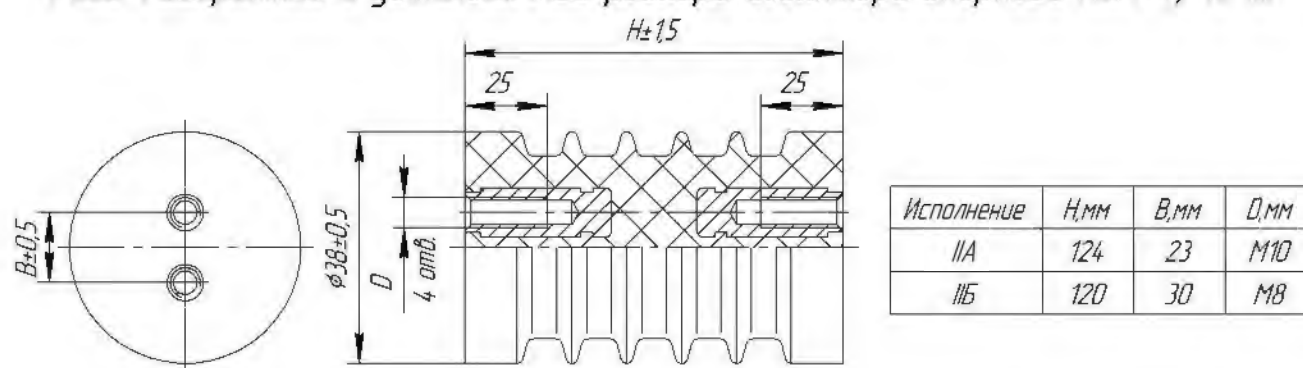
Габаритные и установочные размеры изолятора опорного ИОЛ-4/10 III.
